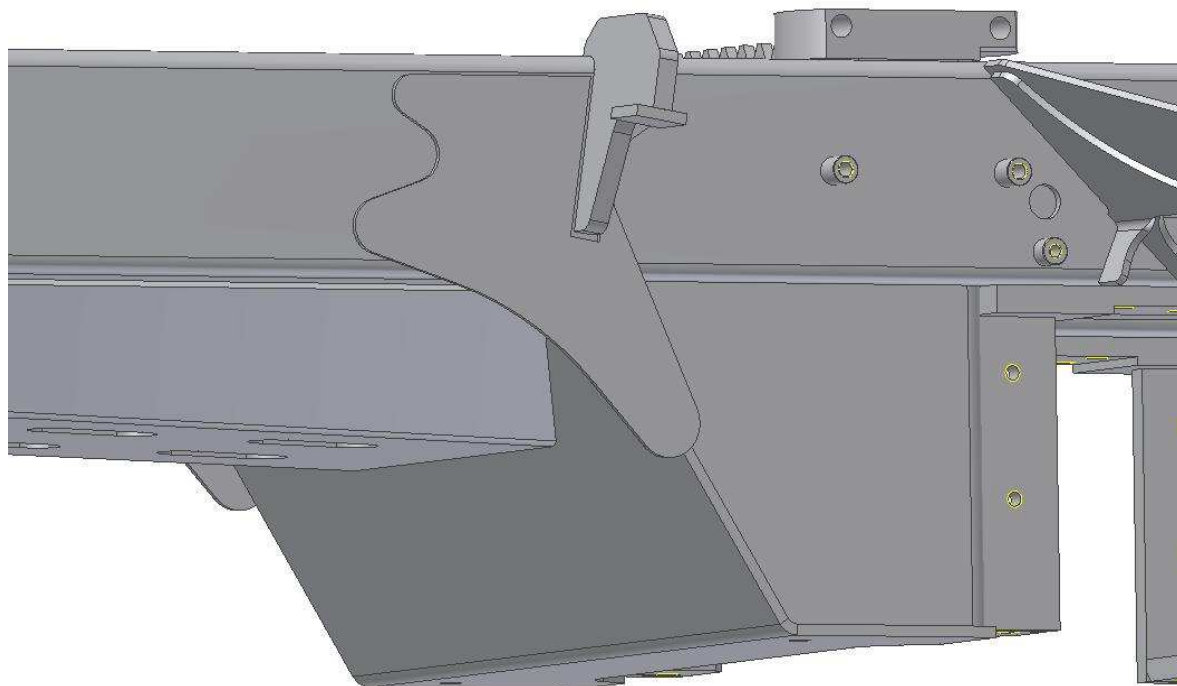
Změna rozmístění žeber držáku (zobrazeno bez horního plechu držáku)
